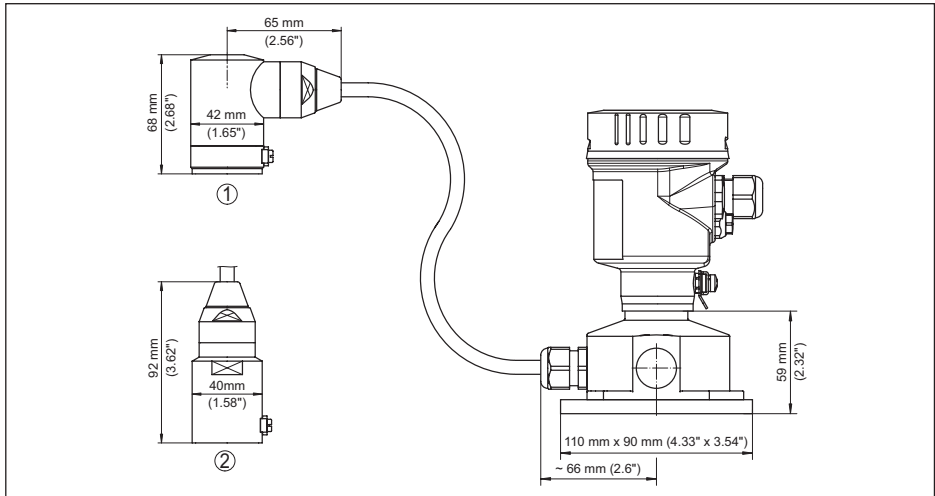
IP 68-Ausführung mit externem Gehäuse - Edelstahl ausführung
